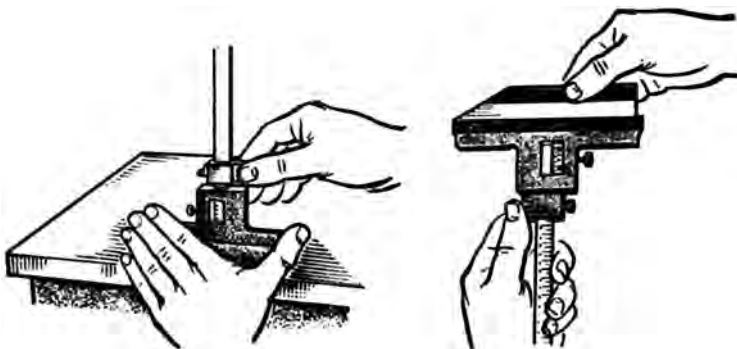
Перевірка нульового положення штангенглибиноміра
